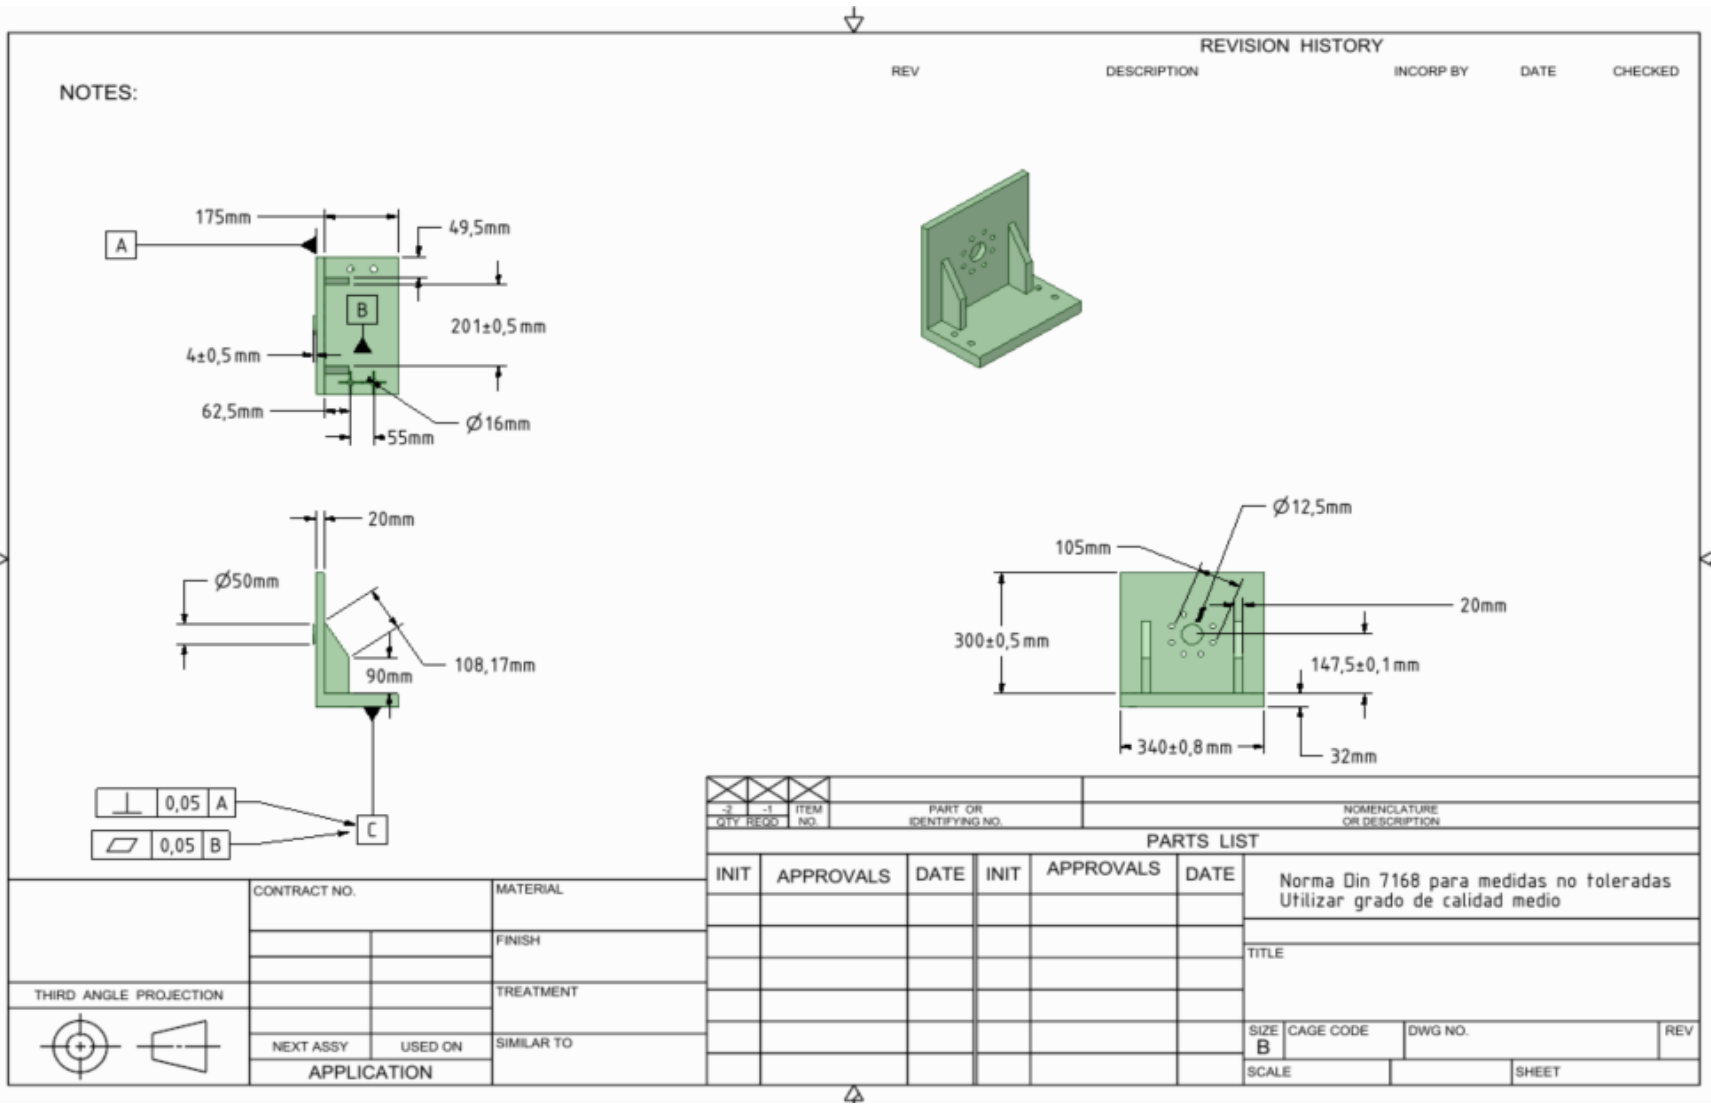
Planos de fabricación de la contrapunta. Fuente: Elaboración propia
